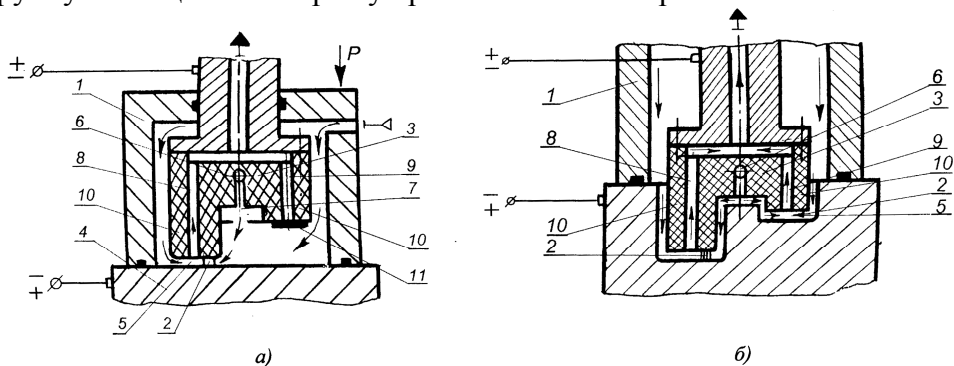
Принципова схема початку (а) і завершення (б) процесу обробки порожнин складного рельєфу
